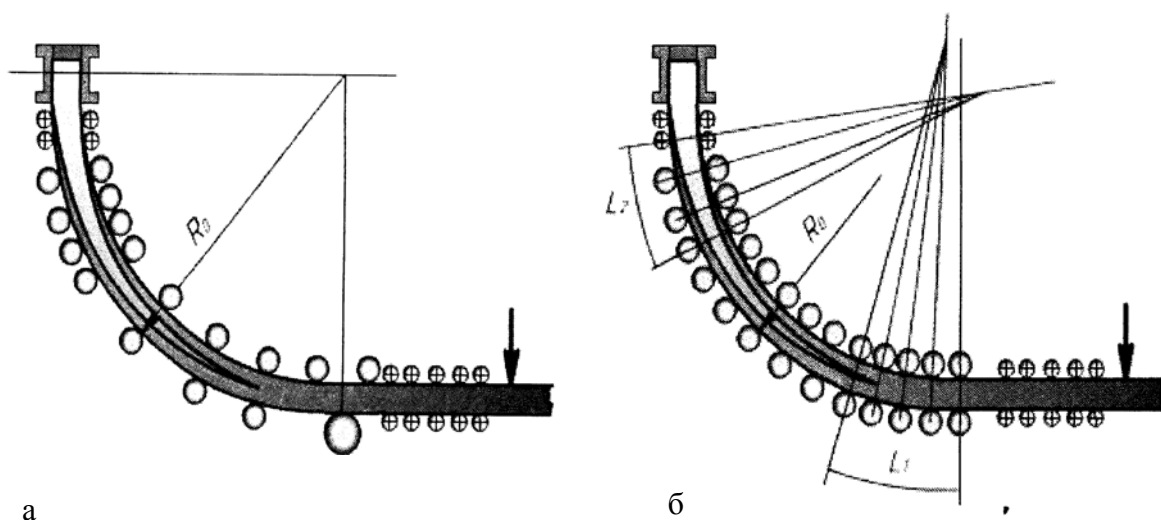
Схемы для разливки сортовых заготовок (а – радиальной, б – криволинейной)
